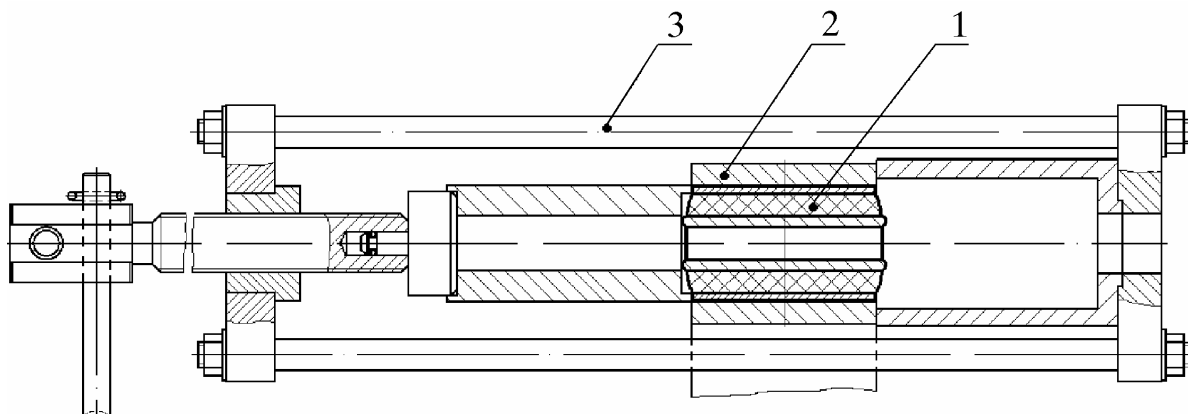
Выпрессовка резинометаллического шарнира из ушка рессоры:
